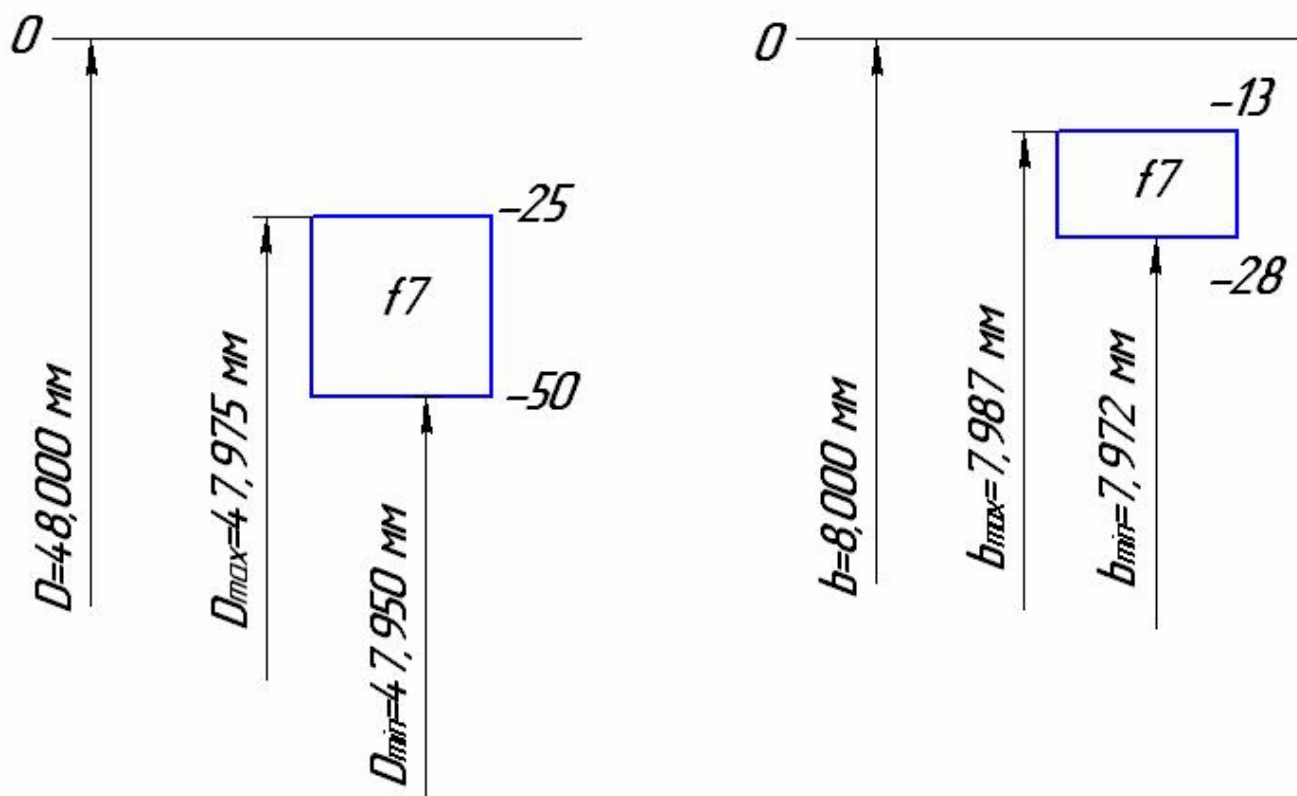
Схемы расположения полей допусков на все элементы шлицевого вала
